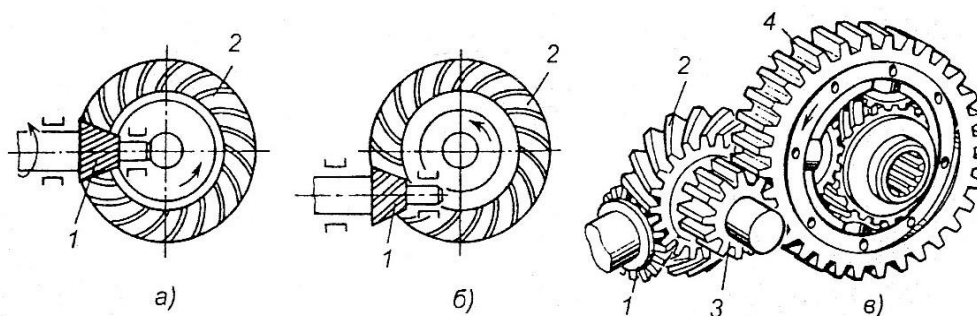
Главные передачи: а – одинарная коническая; б – одинарная гипоидная; в – двойная коническо-цилиндрическая; 1 – ведущая коническая шестерня; 2 – ведомое коническое зубчатое колесо; 3 – ведущая цилиндрическая шестерня; 4 – ведомое цилиндрическое зубчатое колесо
